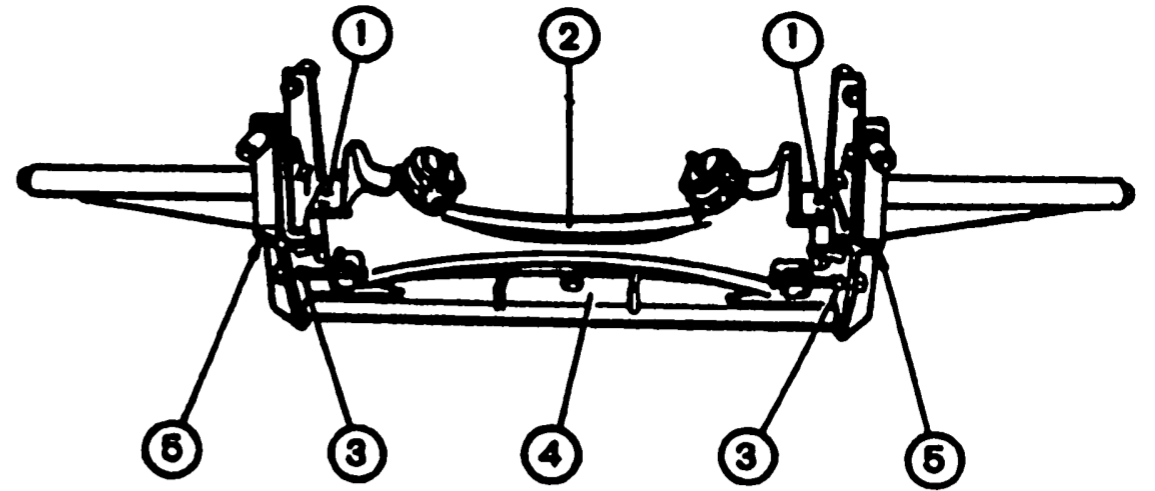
Проверка поперечины передней подвески: 1 - отверстия на поперечине под установочные штыри приспособления; 2 - поперечина; 3 - контрольные втулки приспособления; 4 - приспособление А.78124/R; 5 - контрольные отверстия установки болтов на поперечине
